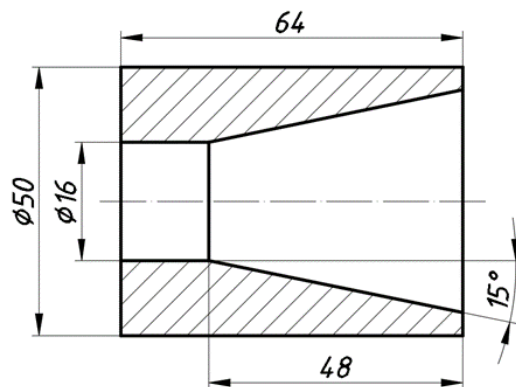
Образец выполнения чертежа детали, имеющей отверстие конической формы.
